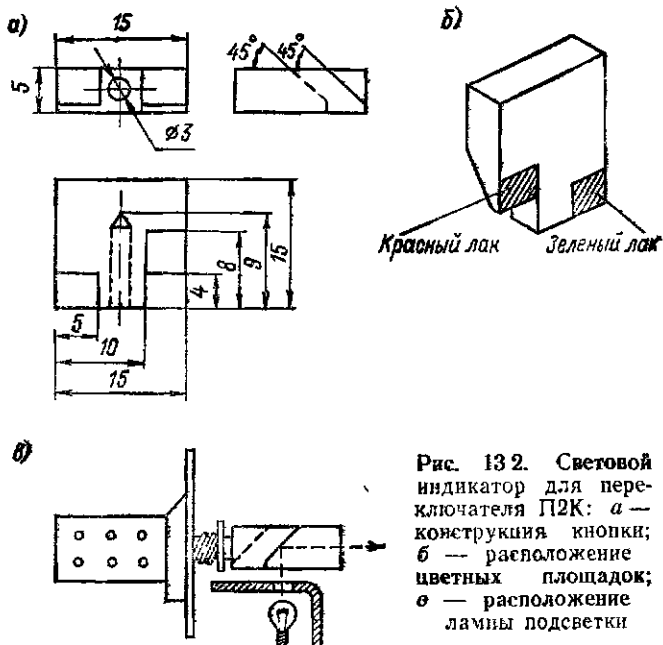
Световой индикатор для переключателя П2К: а — конструкция кнопки; б — расположение цветных площадок; в — расположение лампы подсветки
